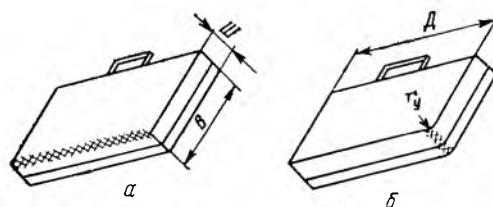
Варианты соединения полотна чемодана с боковыми стенками (а) и стенки с ботаном (б)
